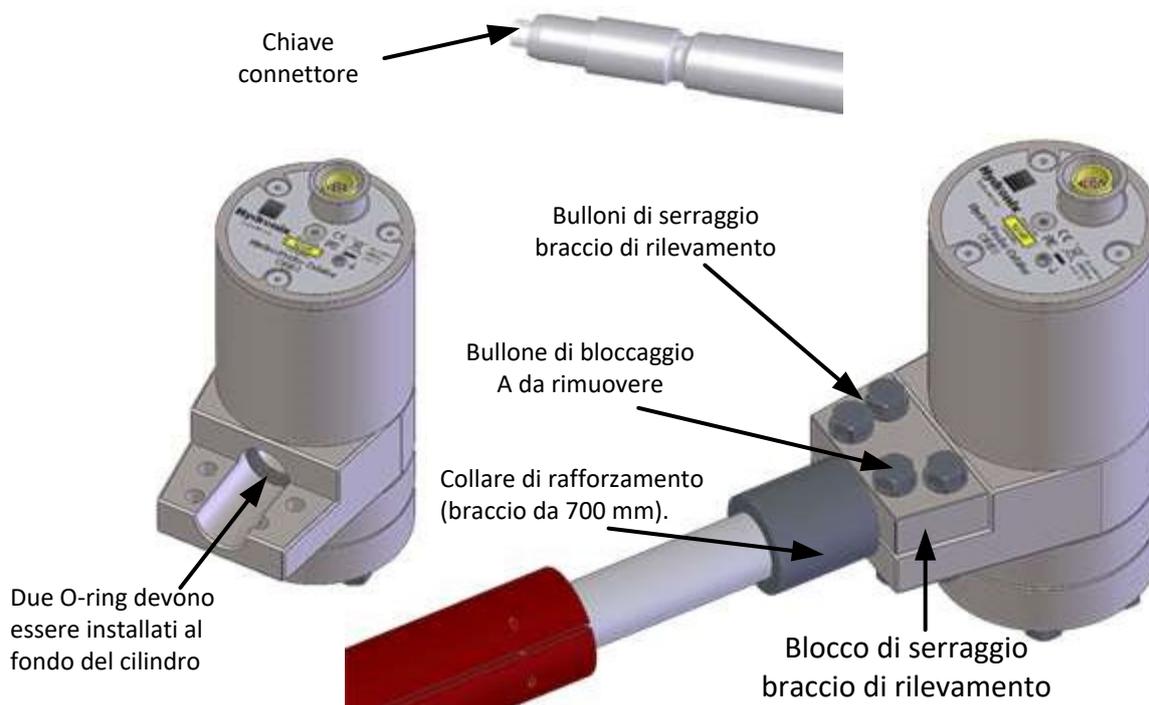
Installazione del braccio di rilevamento nell'unità della testina del sensore
